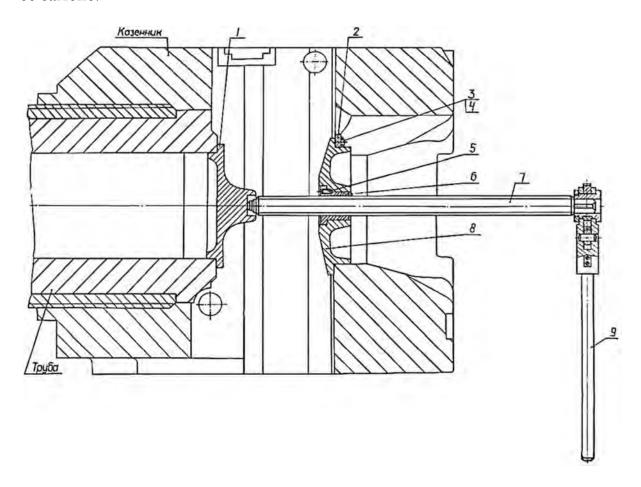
Установка приспособления для выпрессовки трубы: I – передняя опора; 2 – планка; 3, 5, 7 – винты; 4 – проволока; 6 – матка; 8 – задняя опора; 9 – ключ-трещотка РГ 11-1. На изделиях другого варианта детали позиции 3 и 4 исключены
